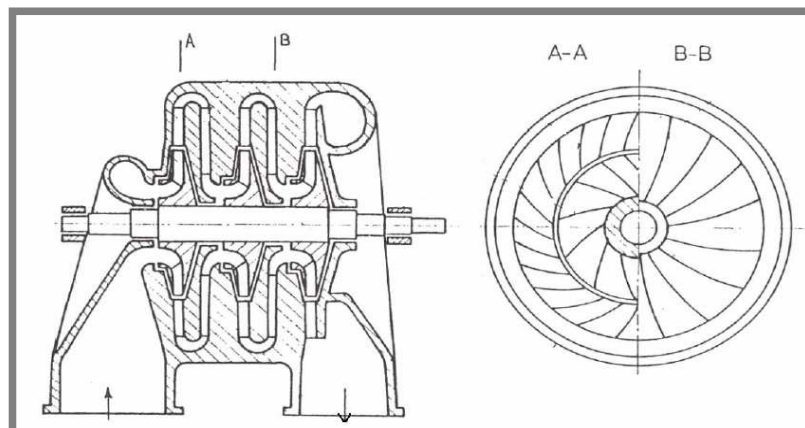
Schéma radiálního turbokompresoru [6]
